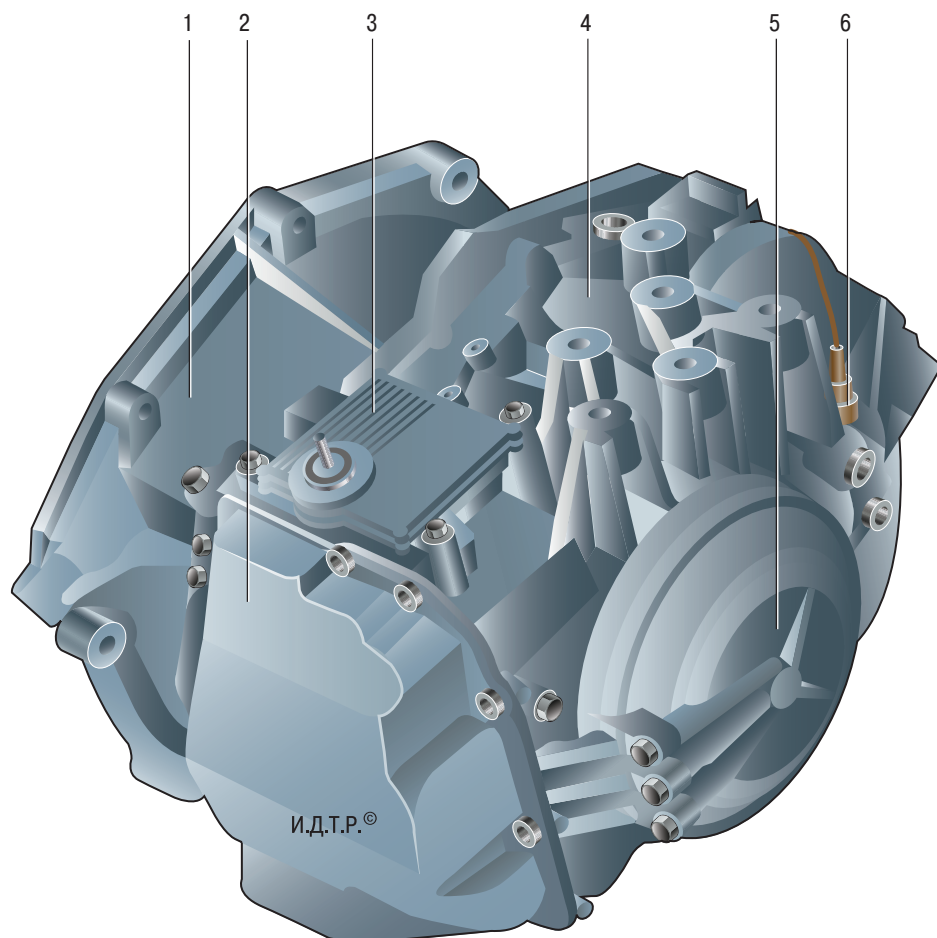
Автоматическая коробка передач: 1 — картер гидротрансформатора; 2 — масляный поддон; 3 — механизм переключения режимов; 4 — картер коробки передач; 5 — крышка; 6 — электрический разъем
